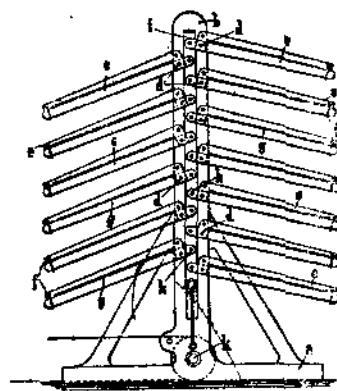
Приспособление для высушивания фанер. Вид спереди.
